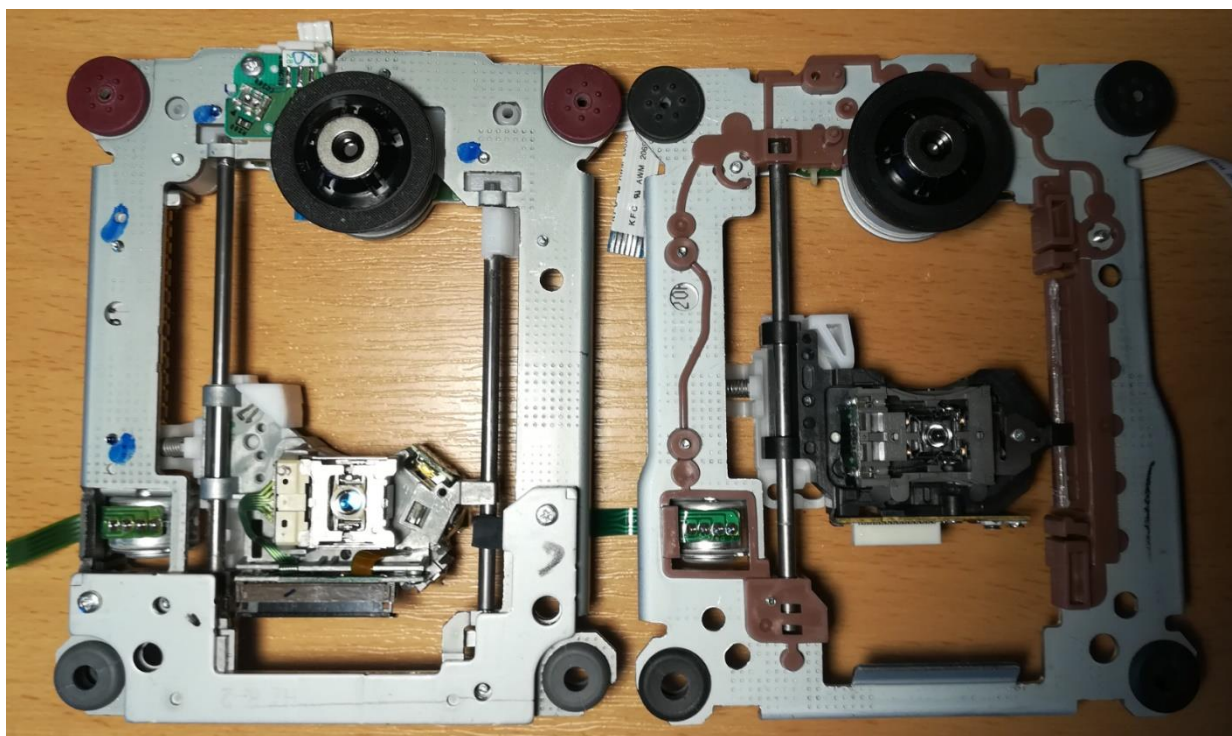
Detail uložení kovového rámu v korpusu v mechanice LG GSA-H12L.
